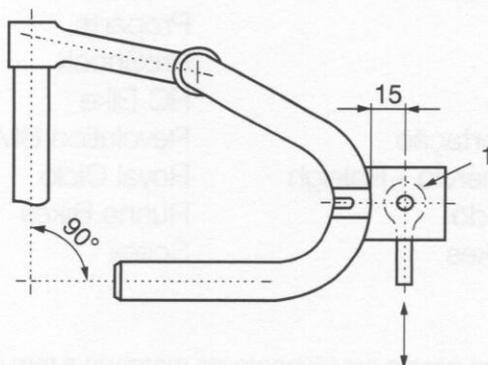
Dispositivo que reproduz a fixação de freio para bicicletas de corrida
